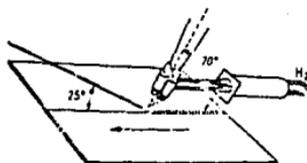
Soldadura con hidrógeno atómico.
